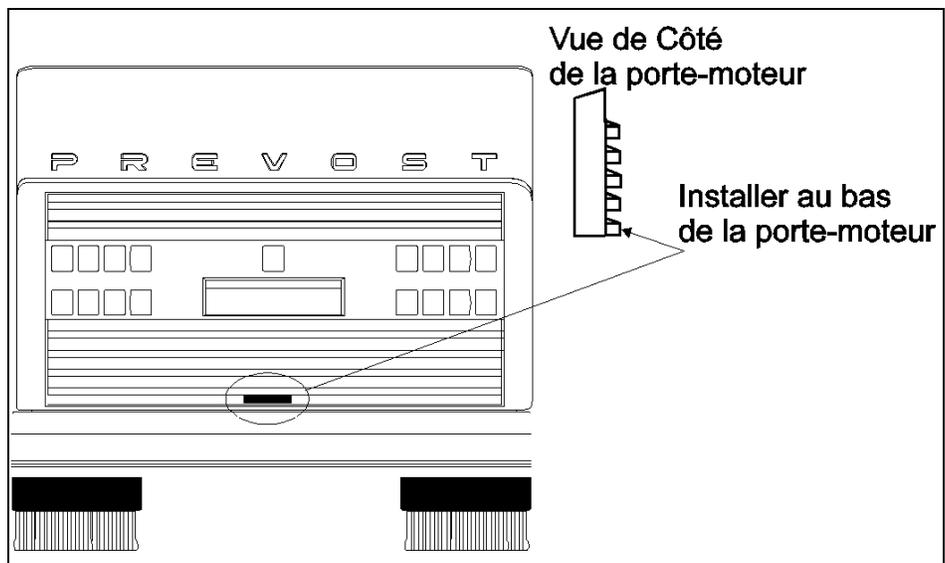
VUE ARRIÈRE D'UNE CARROSSERIE D'AUTOCAR H3
